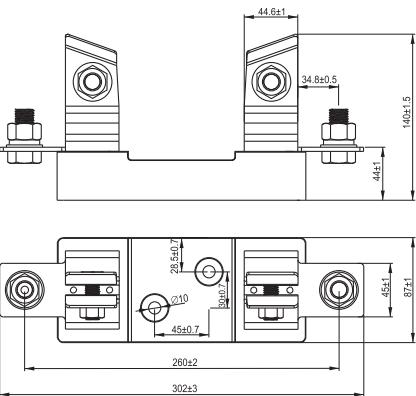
Габаритные размеры держателя плавкой вставки габарита 4 / Figure 3 – Overall dimensions of fuse-carrier, dimension 4
